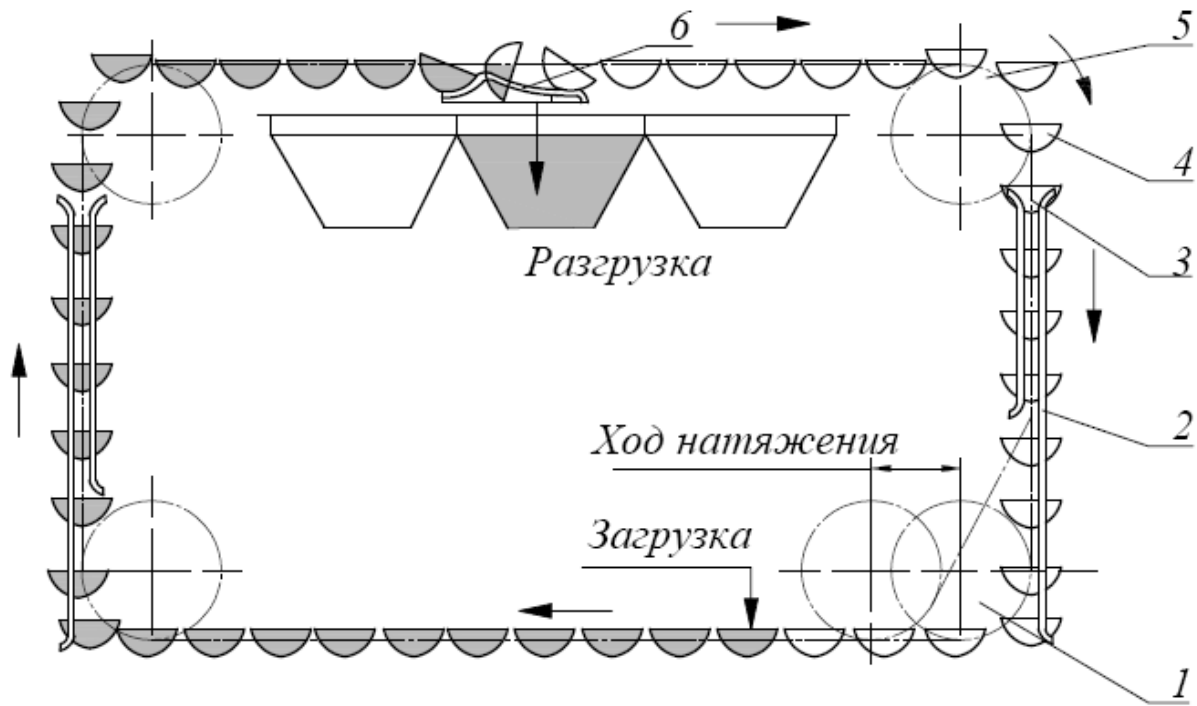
Схема ковшового конвейера: 1 – натяжная звездочка; 2 – направляющая шина; 3 – тяговый орган; 4 – ковш; 5 – приводная звездочка; 6 – разгрузочная шина
